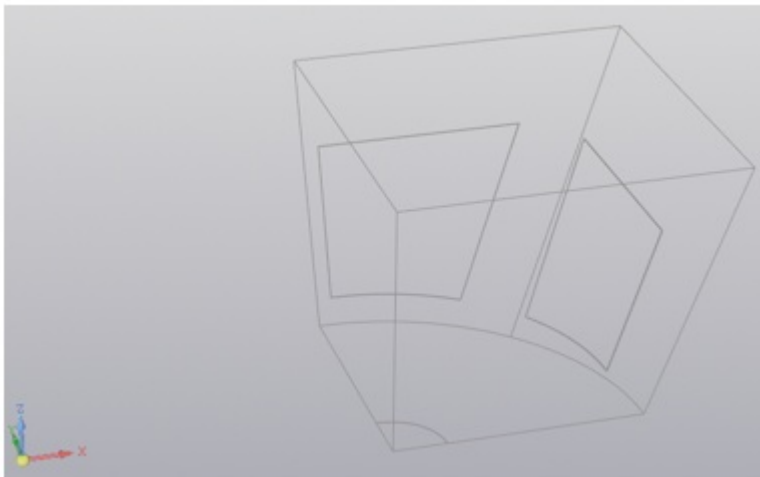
Модернизированный вариант № 2 конструкции диффузора
